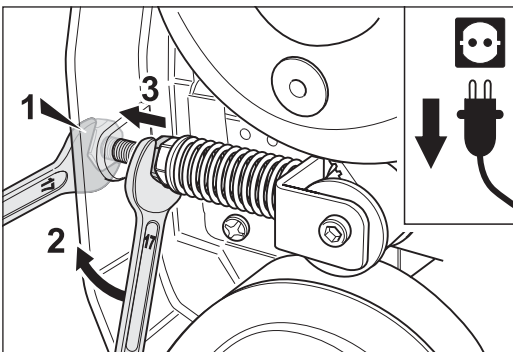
Die Schraube des Zahnriemenspanners mit einem Gabelschlüssel festhalten (1) und gleichzeitig mit einem zweiten Gabelschlüssel die Kontermutter bis an die Innenwand der Schleifhaube schrauben (2 + 3).
